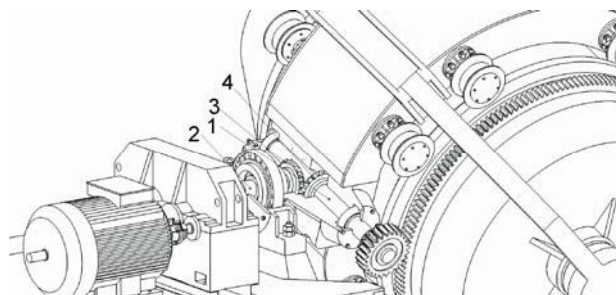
Предложенная конструкция механизма вращения корпуса кислородного конвертера
